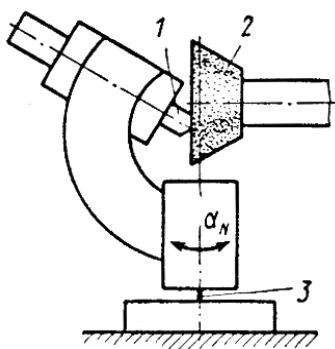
Приспособление для двухплоскостной заточки сверла:
